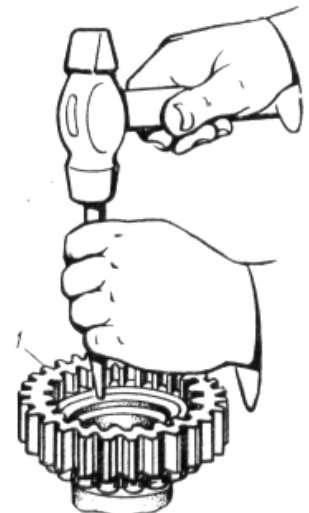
Випресування підшипника ведучої шестерні II ступені редуктора: 1- ведуча шестерня.
